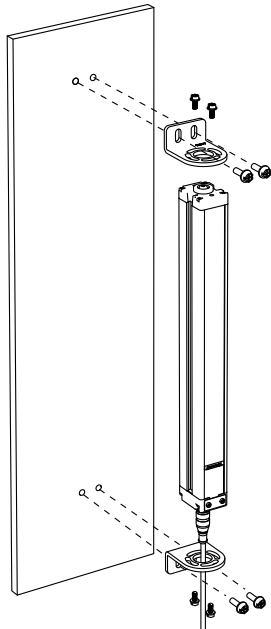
Montage latéral (remplacement possible par deux équerres de capteur)
